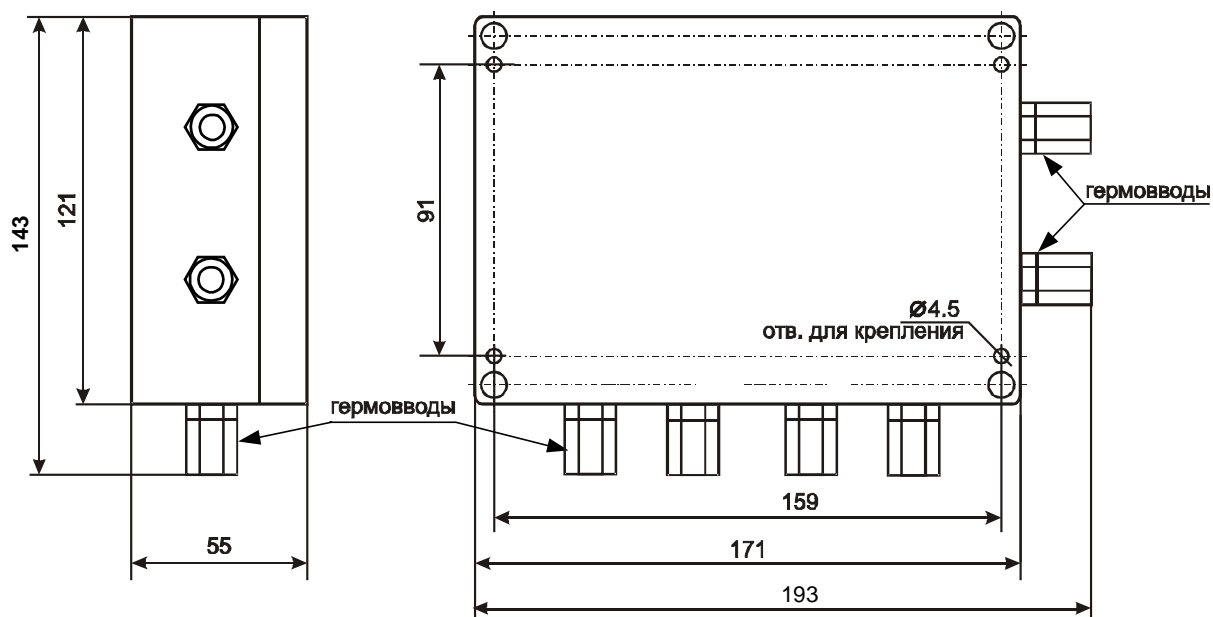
Габаритные и присоединительные размеры СК-01 исп.3 в корпусе IP65
